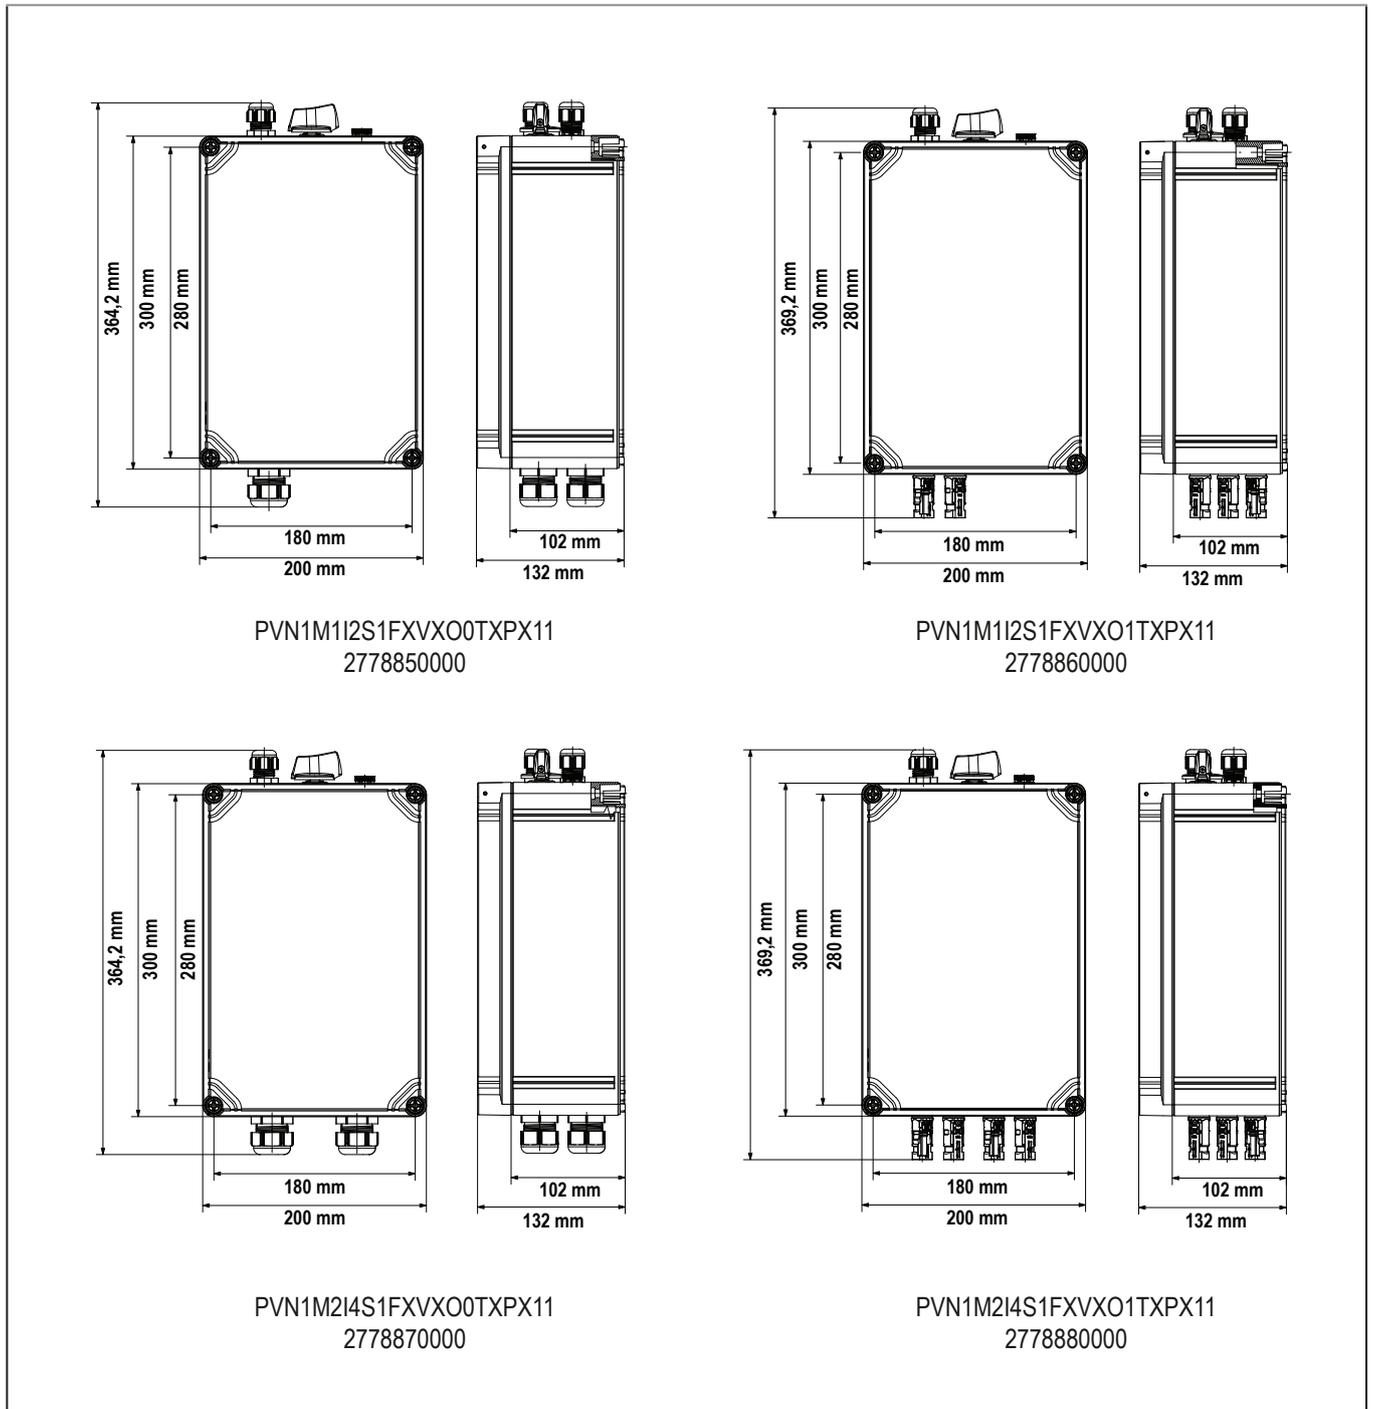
Maße für Direktmontage ohne Befestigungslaschen
